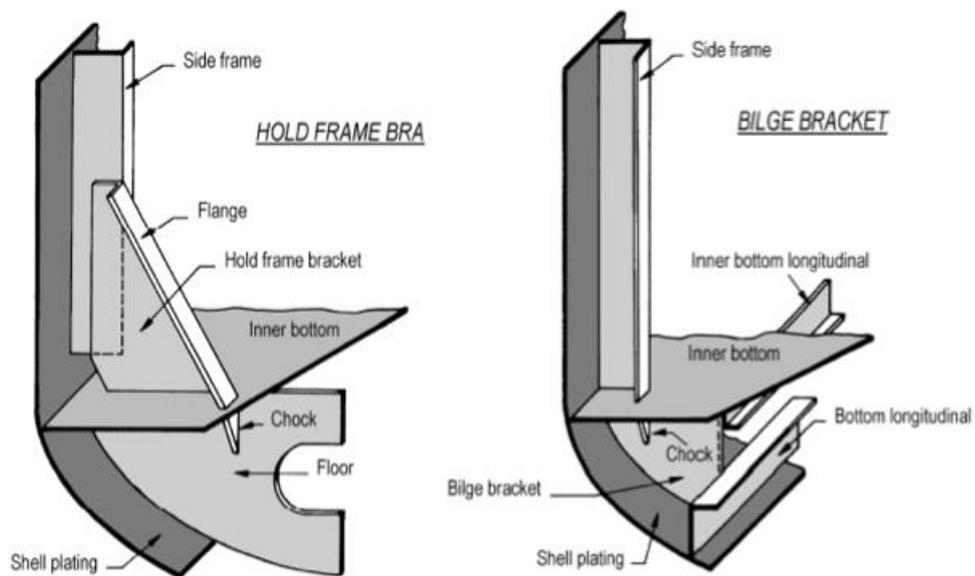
Configuración estructural y detalles – escuadra de conexión superior
